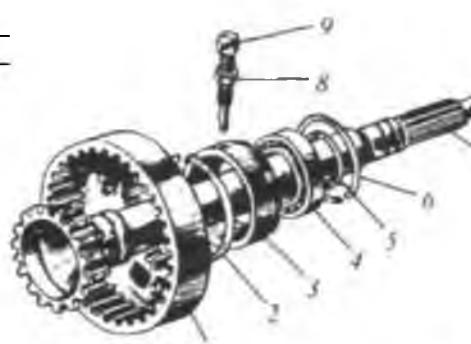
Коронна шеперня в розібраному вигляді: 1 - коронна шестерня; 2 - стопорне кільце 2В110; 3 - стакан/підшипника; 4 - шариковий підшипник 210А; 5 - стопорне кільце 2В50; 6 - стопорне кільце 2В90; 7 - вал; 8 - гайка М12; 9 – гвинт.
